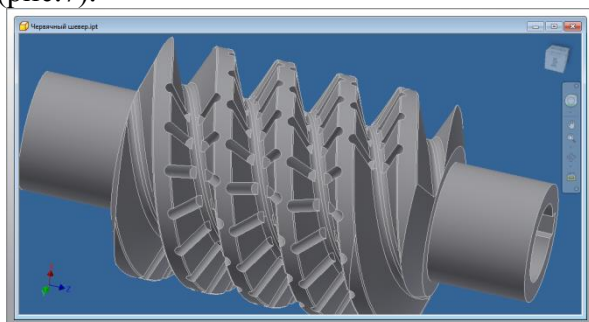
Трехзаходный червячный шевер с цилиндрическим канавками
